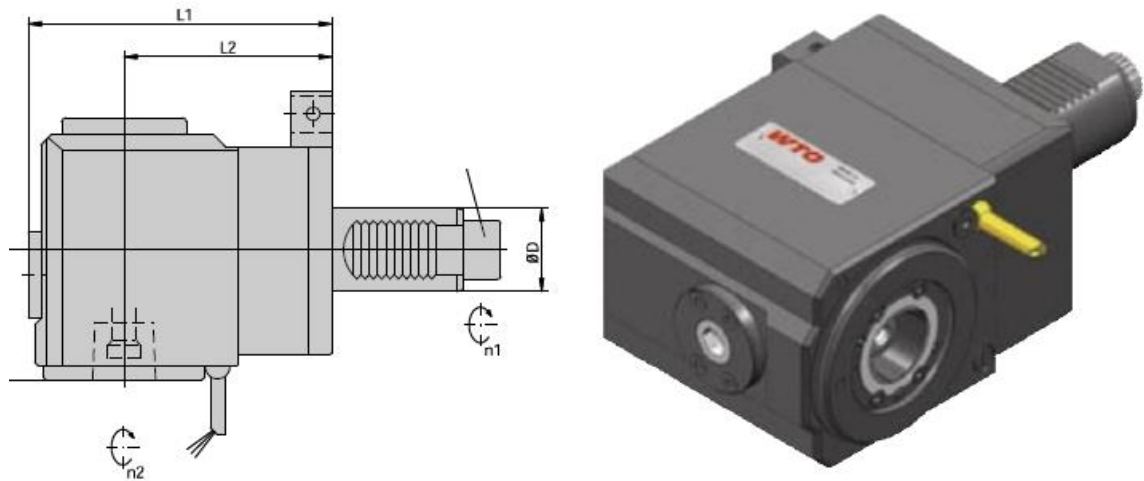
Кутвий свердлильно – фрезерний блок.
